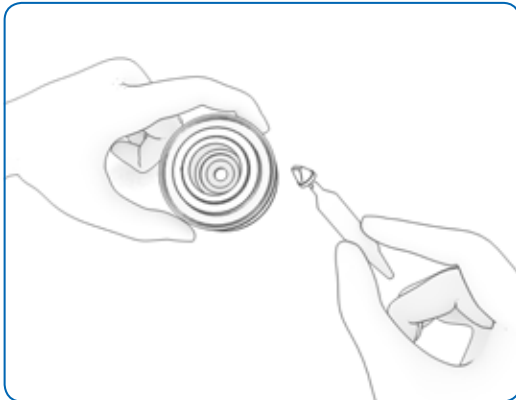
Entfernen des Rückschlagventils mithilfe des Werkzeugs – Teil 2
